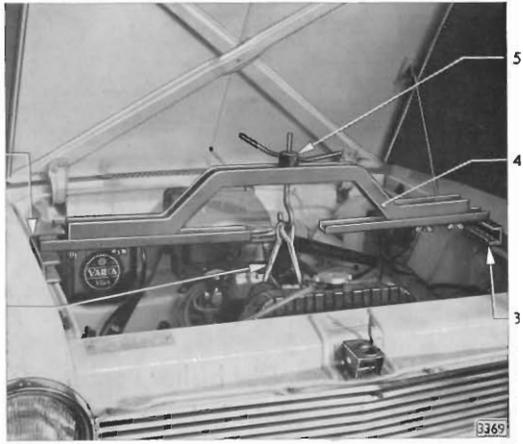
Motorheber S-1244 auf Radeinbau aufgesetzt
